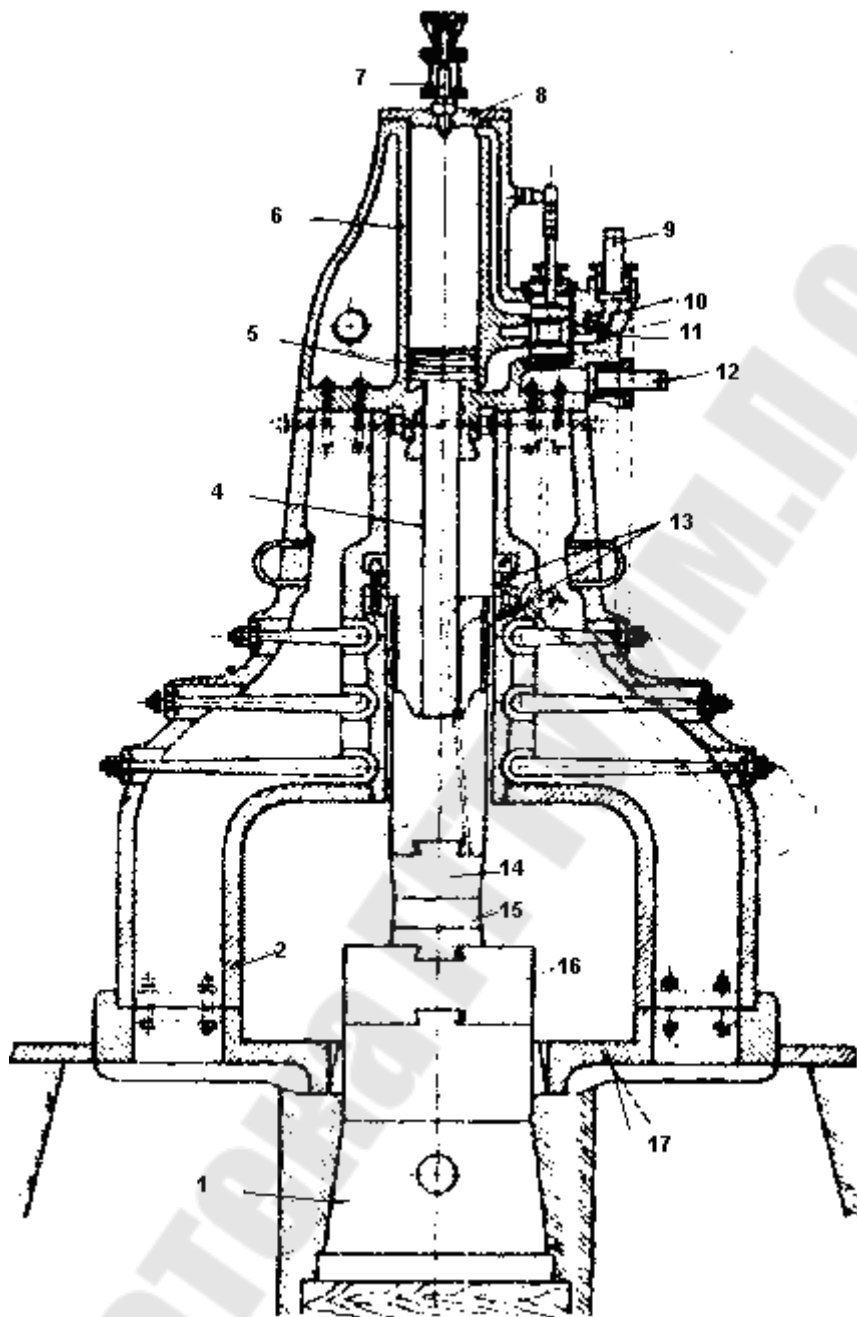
Паровоздушный двухствочный ковочный молот двойного действия со станиной арочного типа: 1 - шабот; 2 - стойка станины молота; 3 - баба; 4 - шток; 5 - поршень; 6 - цилиндр; 7 - предохранитель; 8 - крышка цилиндра; 9 - труба свежего пара; 10 - золотник; 11 - дроссель; 12 - обратная труба; 13 - направляющие; 14 - верхний боек; 15 - нижний боек; 16 - подушка; 17 - фундаментная плита
